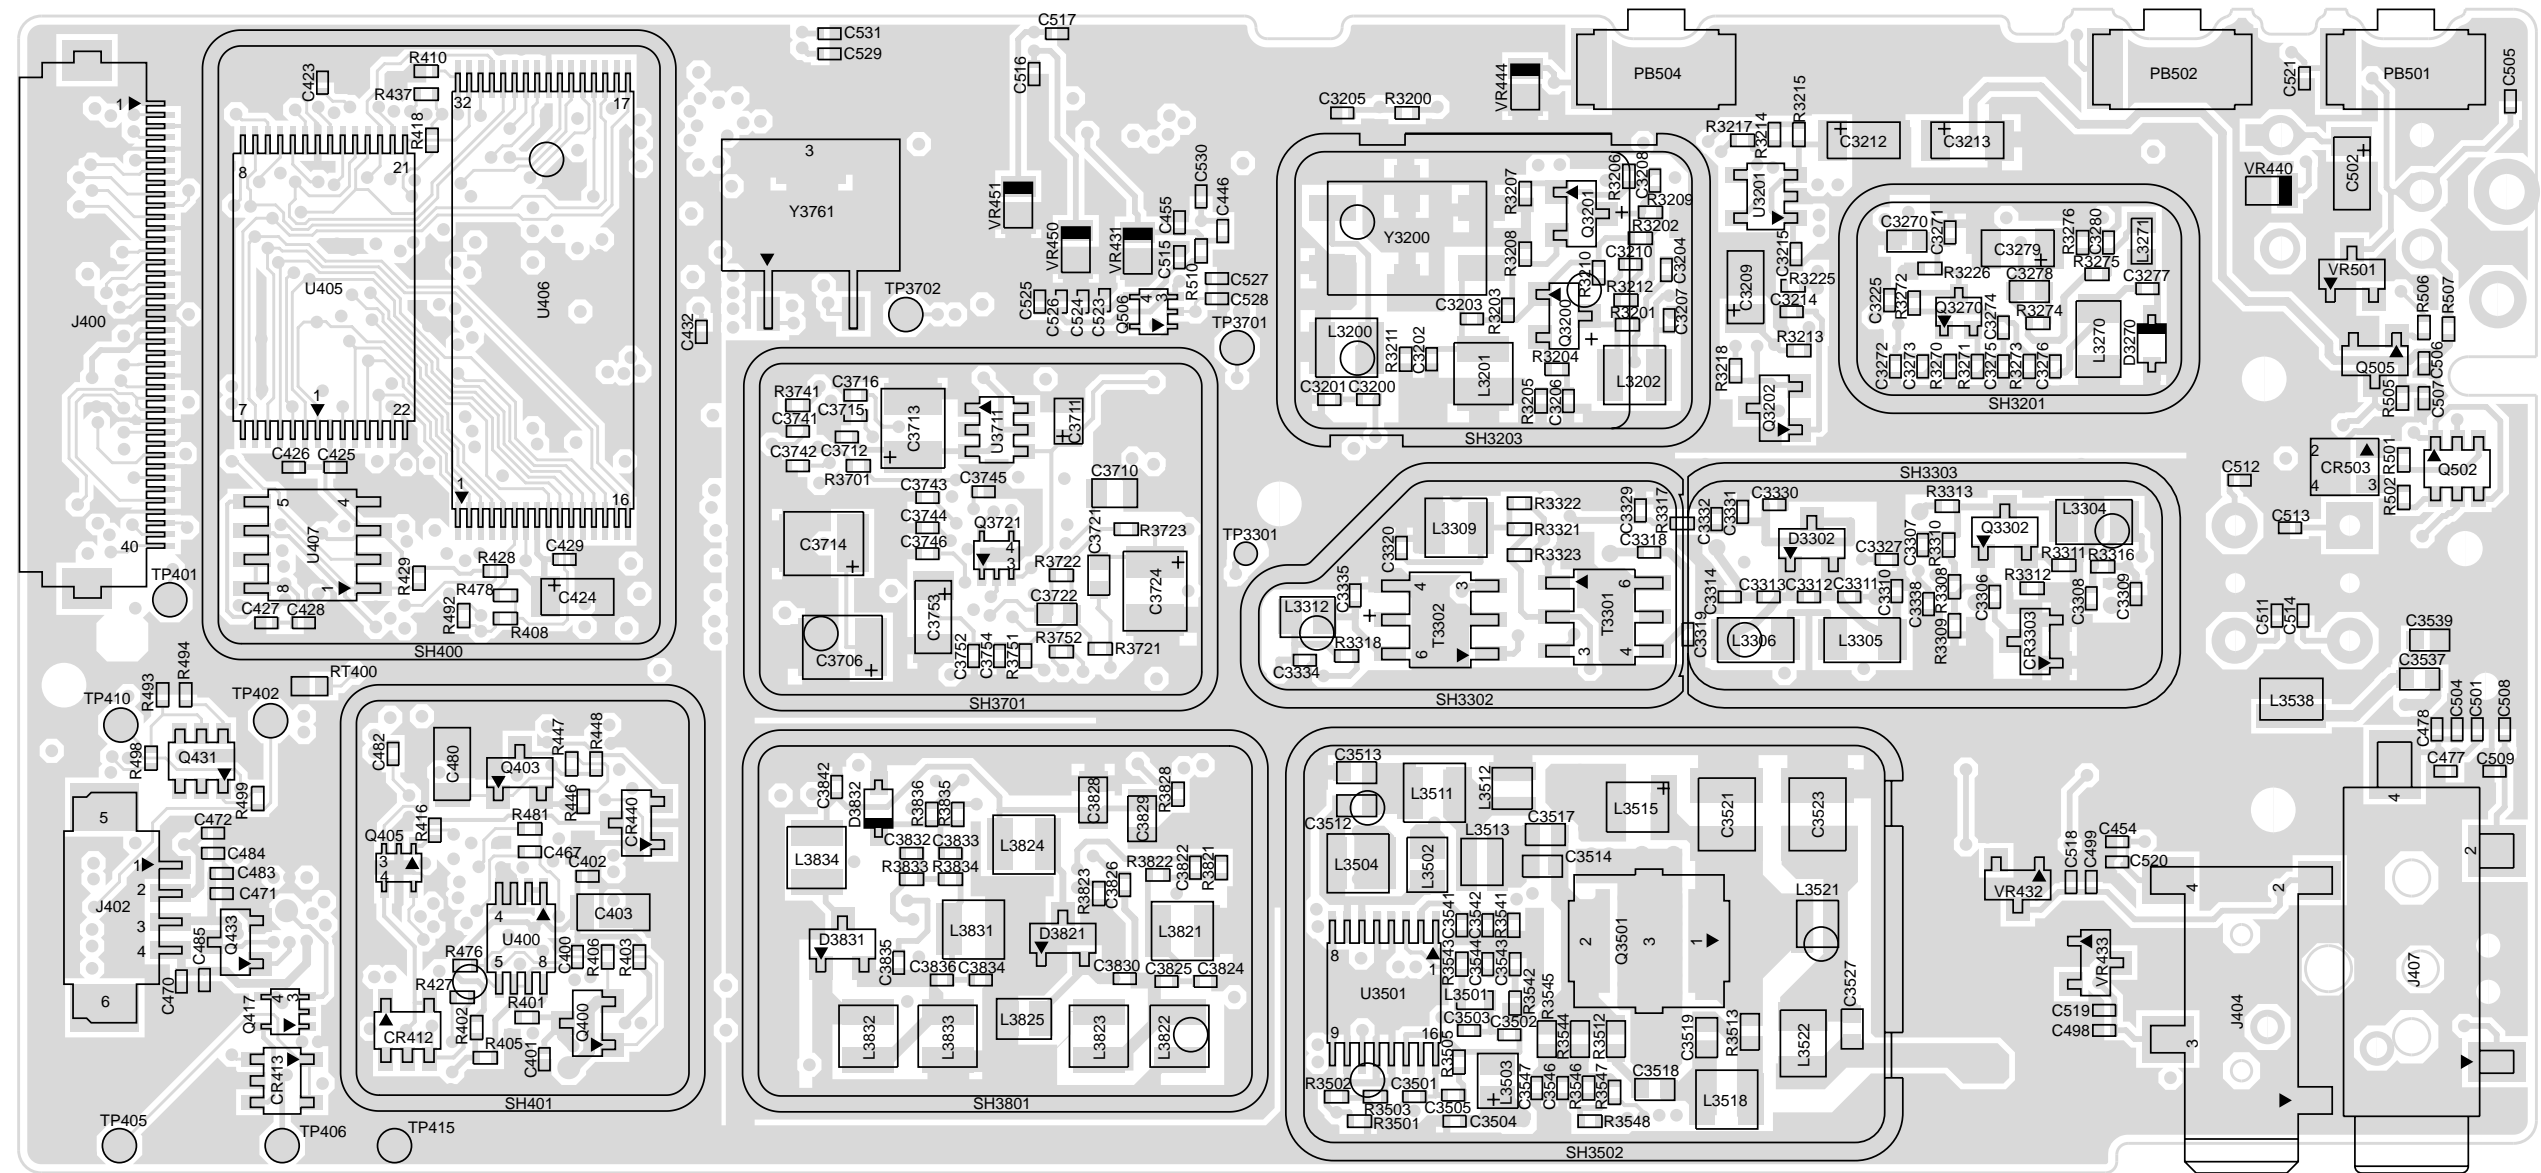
Circuito impreso de la tarjeta principal de VHF (136-174MHz)-Lado Superior
